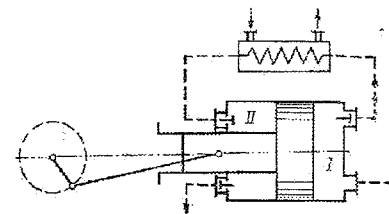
Схема двухступенчатого компрессора прямого типа с дифференциальным поршнем
